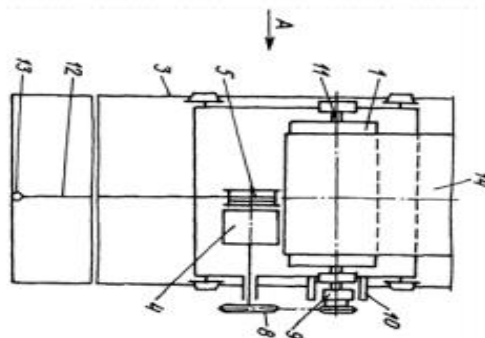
Конструкція натяжного пристрою за патентом RU 2458842
